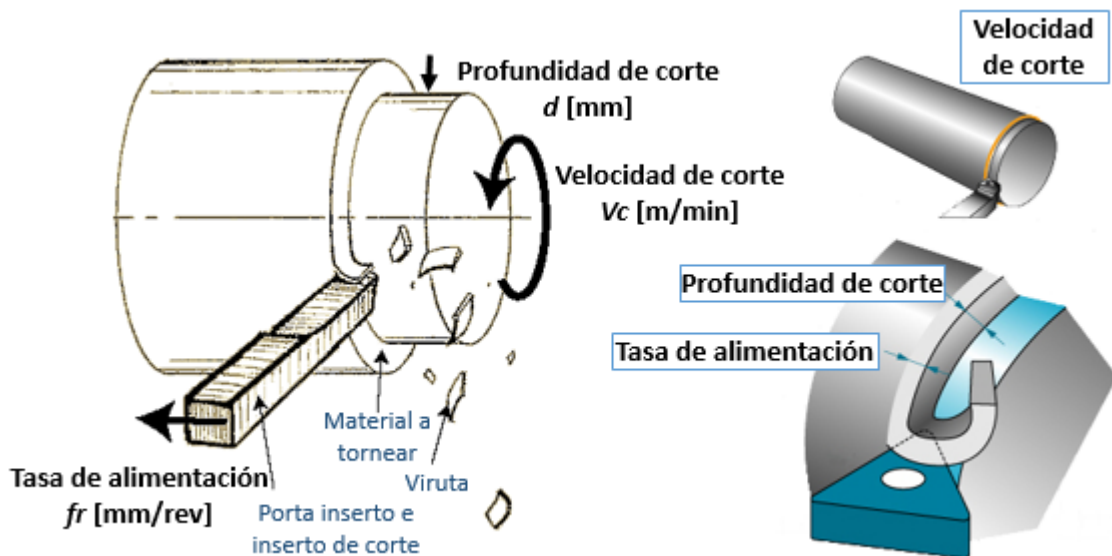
Parámetros de corte en el proceso de torneado. Imágenes adaptadas de: izquierda [2], derecha [3].
